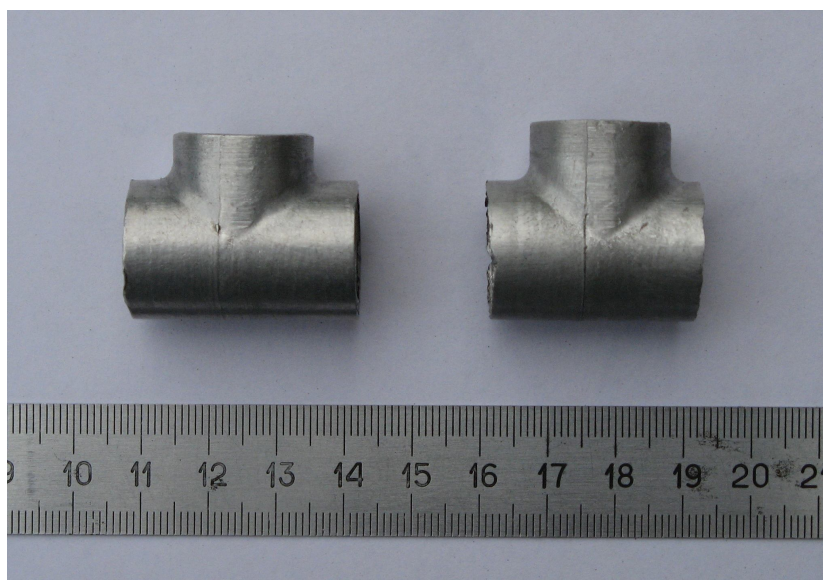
Детали, полученные предлагаемым методом однопереходной штамповки из разных типов заготовок: слева – заготовка с ровными кромками, справа – заготовка со скошенными кромками при прочих равных условиях
